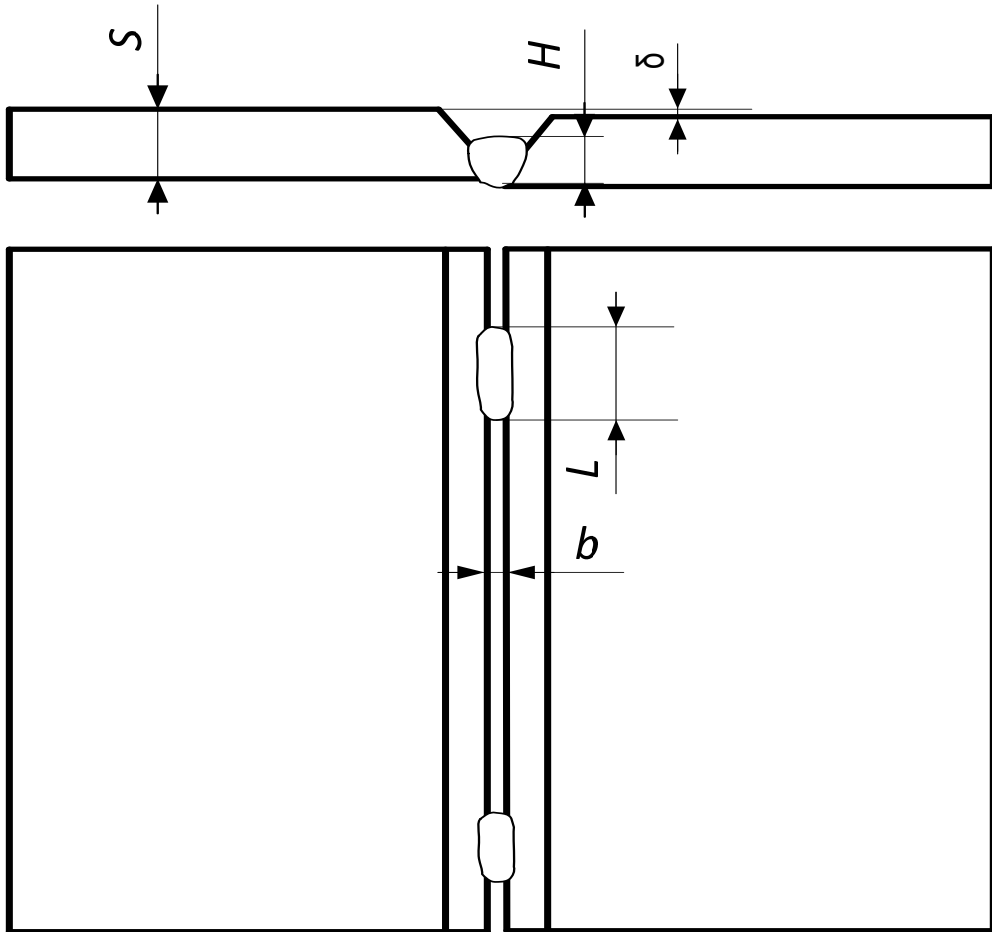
Эскиз контролируемого изделия при контроле сборки деталей под сварку (пластин)
